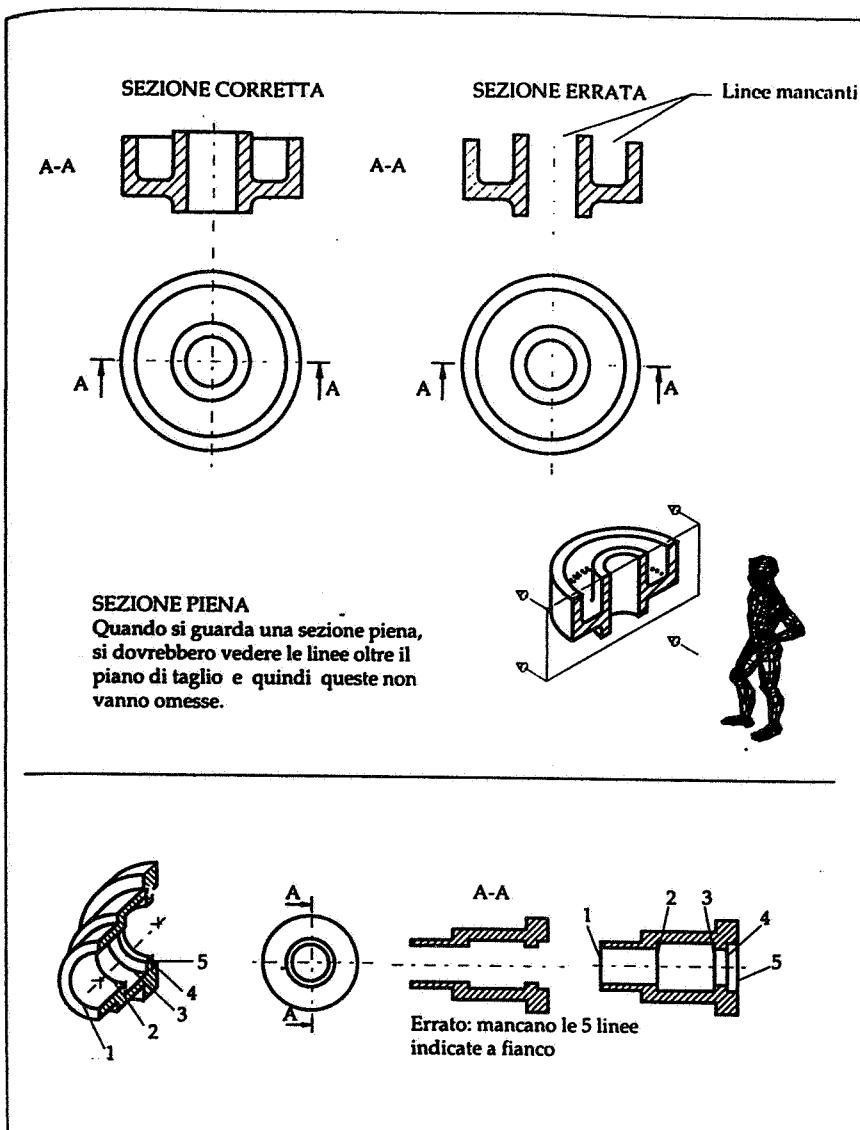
Un errore tipico nell'esecuzione di sezioni: l'omissione del profilo delle superfici coniche o cilindriche intersecate dal piano di sezione.
